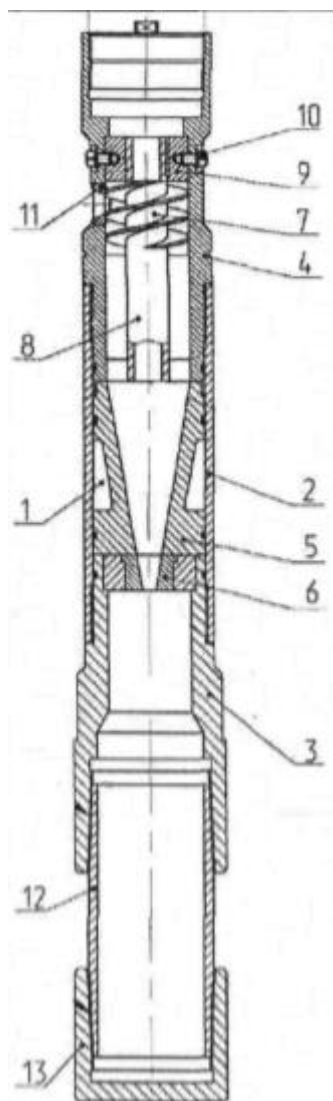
Циклонный десендер СМГБ 1-гидроциклон, 2- корпус, 3- переходник, 4- цилиндрическая головка, 5- конус, 6- разгрузочная насадка, 7- шнек, 8- сливной патрубкок, 9-вставка, 10- упорный винт, 11-насадка, 12- переходник, 13-заглушка.
